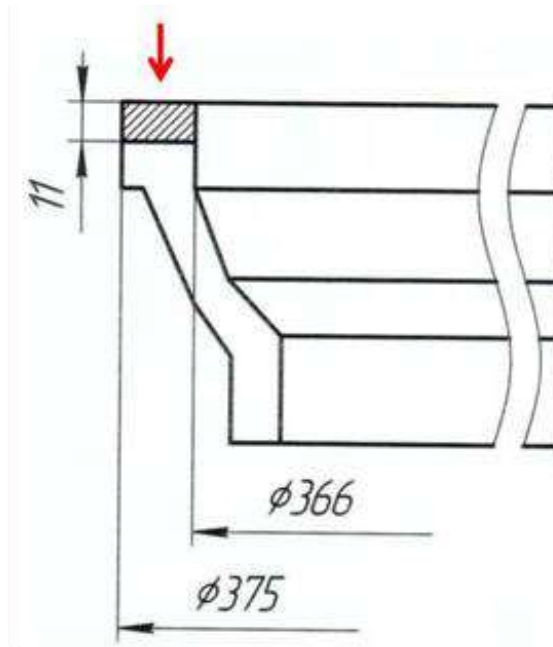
Схема наплавлення 9-ї ділянки
